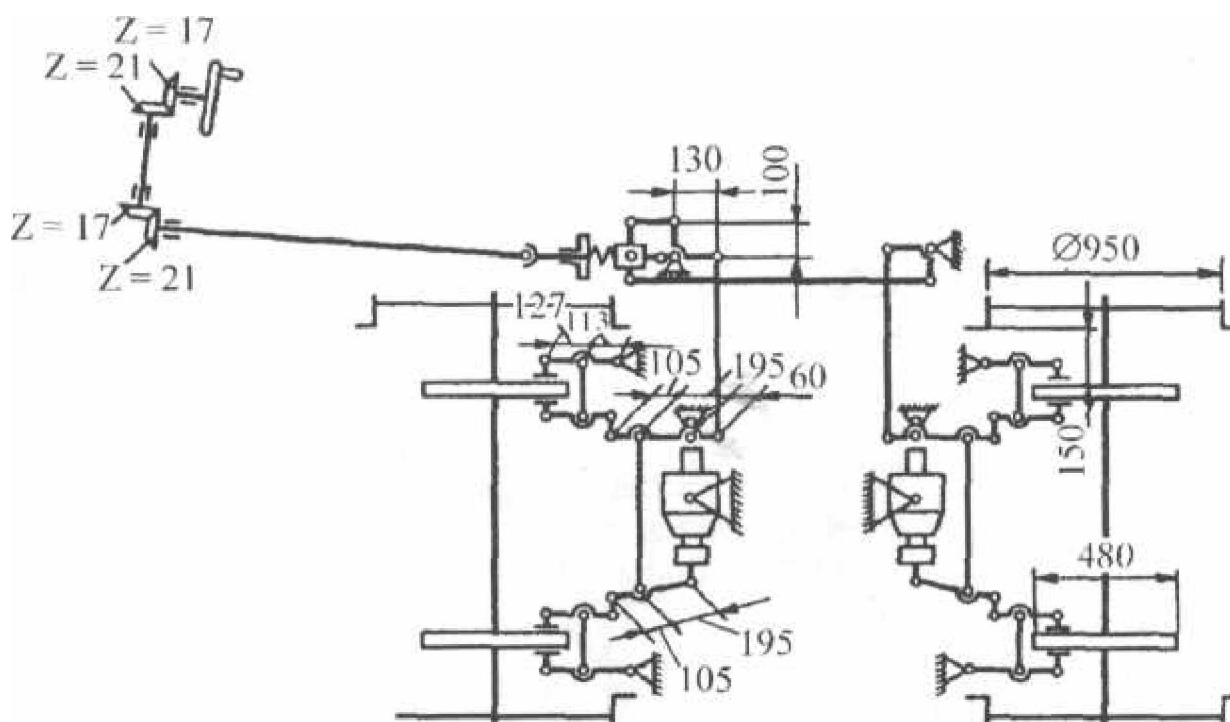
Схема рычажной передачи дискового тормоза пассажирского вагона
